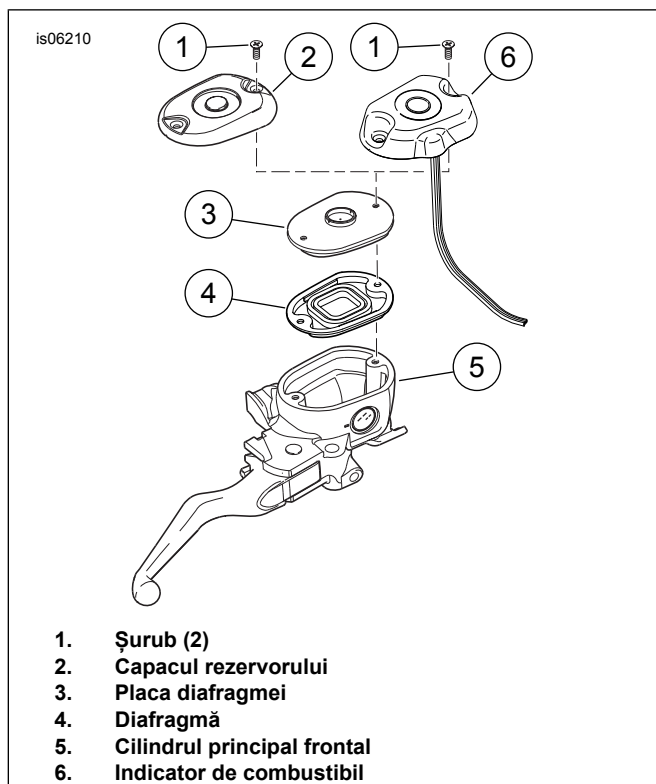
Montați indicatorul de combustibil la cilindrul principal frontal
